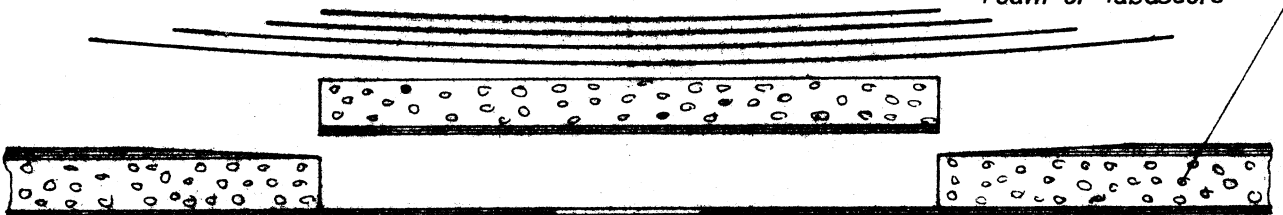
Reparatur der Klasse 2 (Innenseite unzugänglich)
